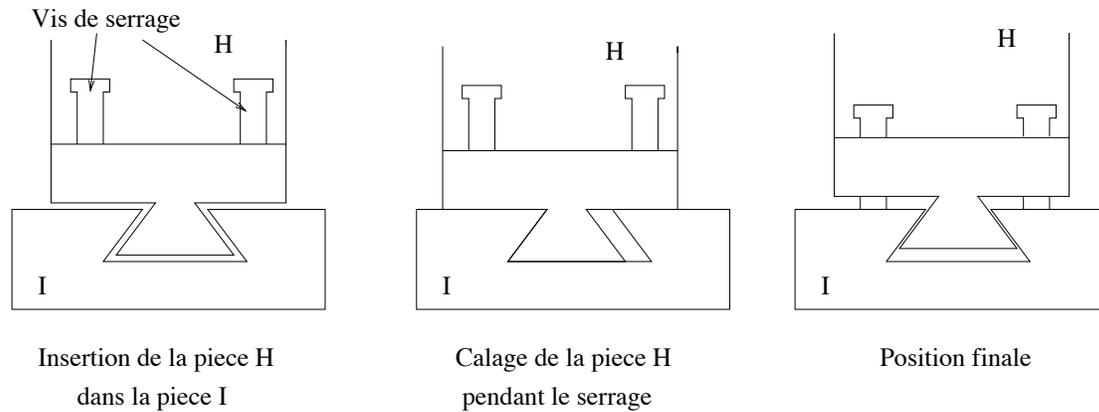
Insertion de la pièce H dans la pièce I. Les dimensions ne sont pas réalistes.
